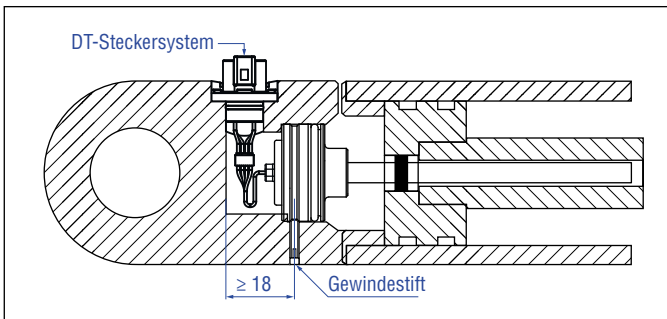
Beispiel für eine In-Zylinder-Montage mit DT-Stecker
